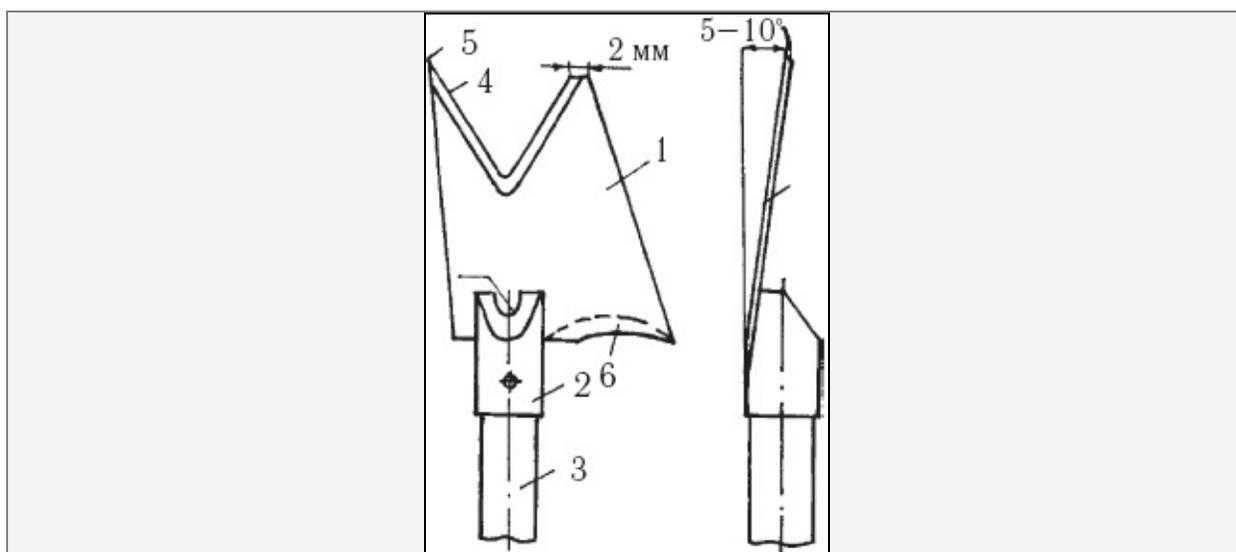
Вилка: 1 – режущая пластина; 2 – соединительное устройство (раструб); 3 – рукоятка; 4 – У-образное лезвие; 5 – удлиненный выступ; 6 – нижнее (вогнутое) лезвие
